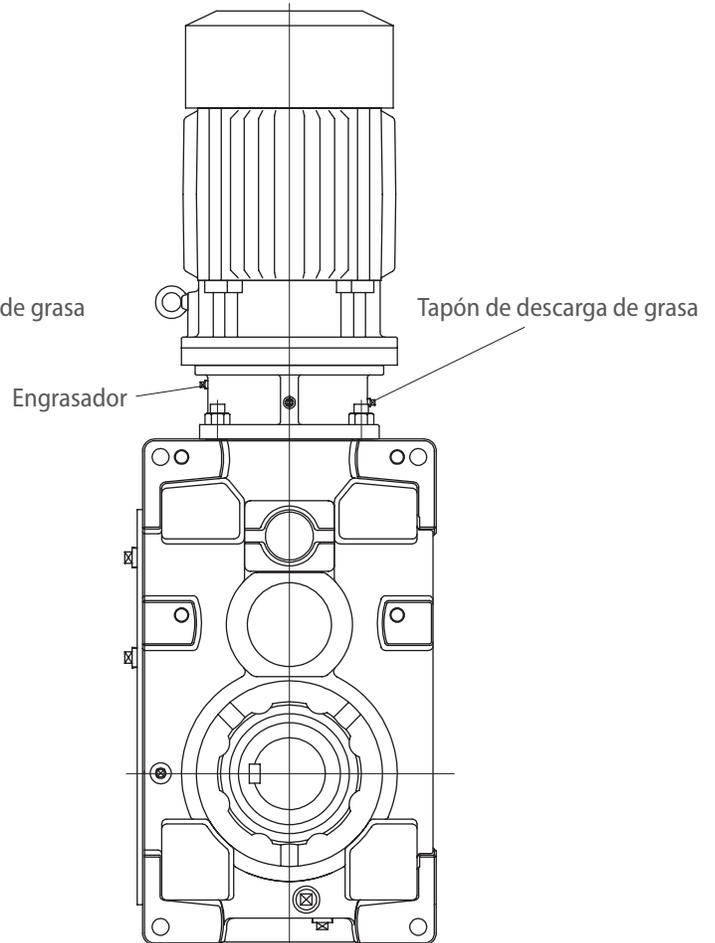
Unidad de accionamiento, montaje perpendicular
